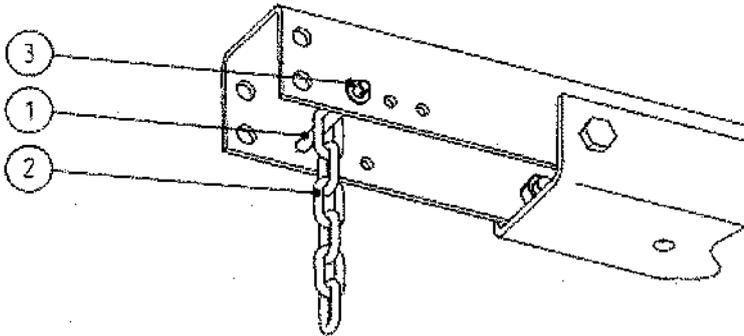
Крепление цепи компенсирующей к нижней балке противовеса: 1 - Ось; 2 - цепь; 3 - шайба и шпилька.
